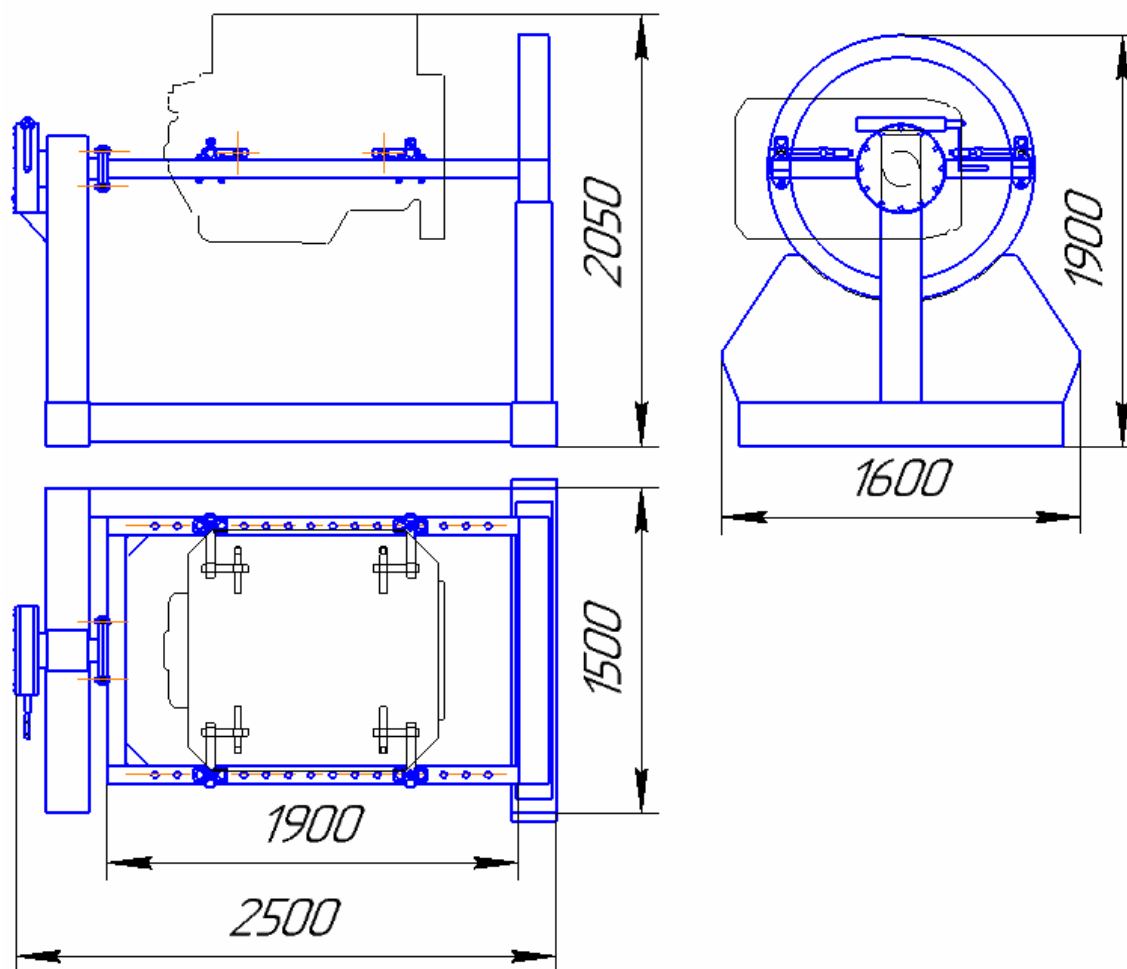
Общий вид модернизированного стенда для разборки и сборки двигателей и агрегатов
